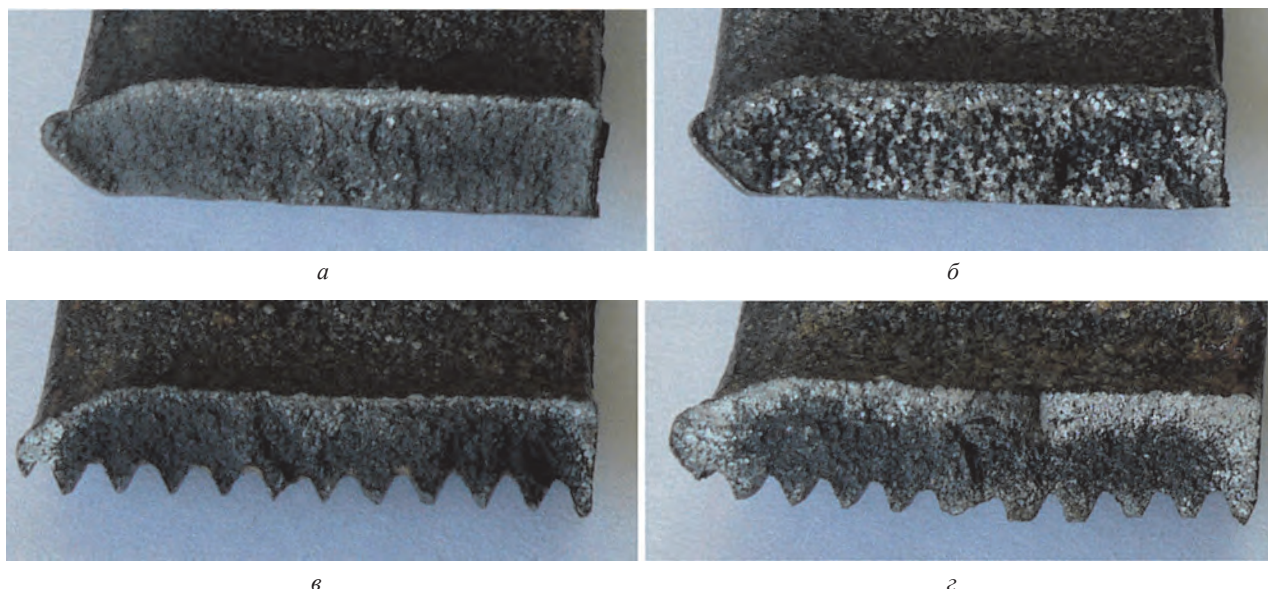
Изломы ниппелей из ковкого чугуна КЧ30-6. $\times 3$: *а* – ковкий чугун по всему объему отливки; *б* – вкрапления белого чугуна по всему объему отливки; *в*, *г* – отбеленный слой на поверхности отливки
